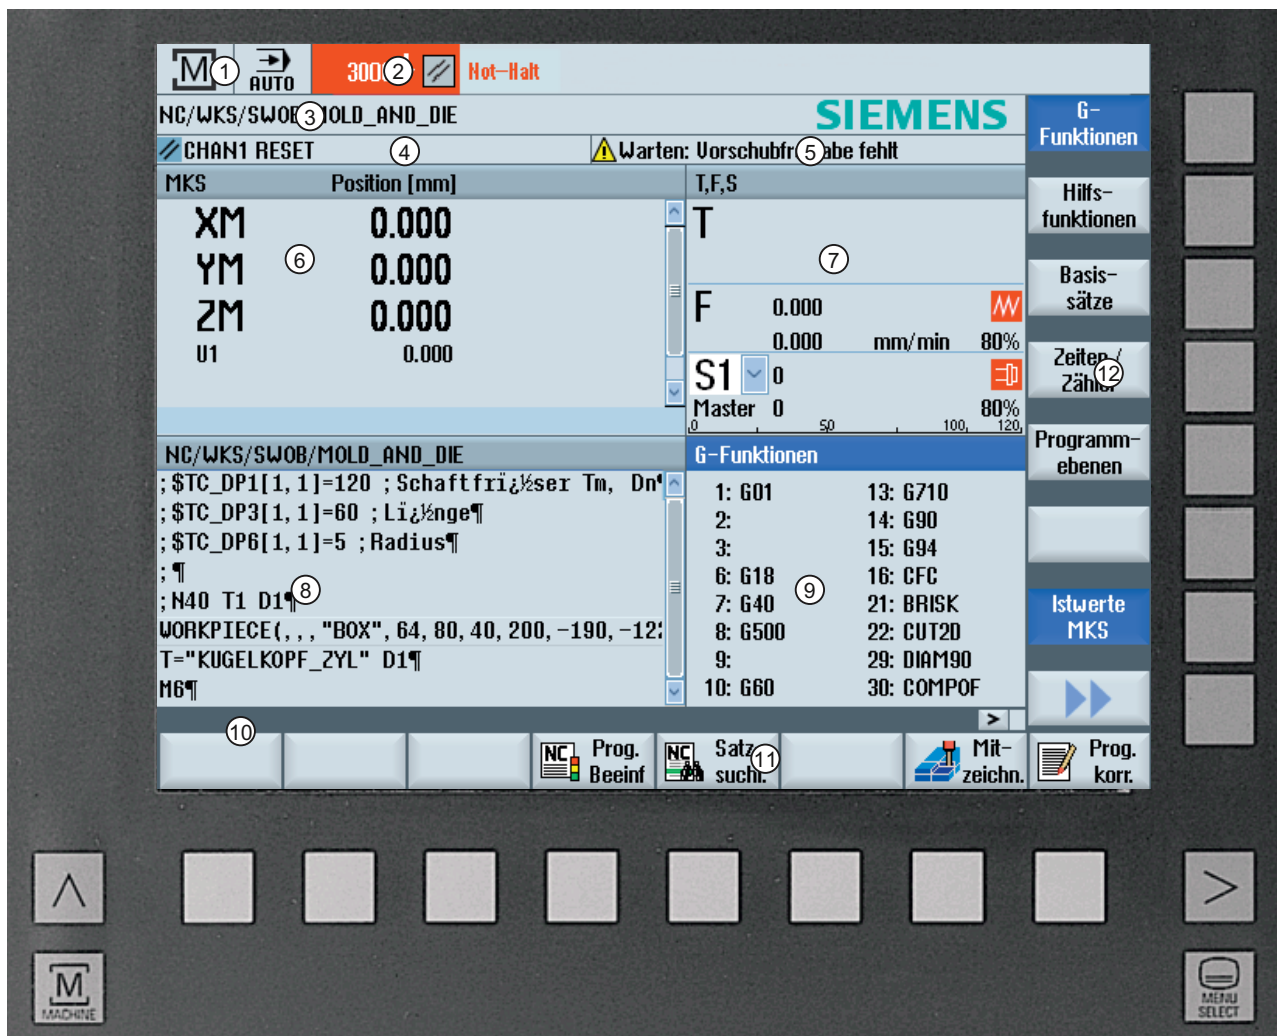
Vorderansicht Maschinensteuertafel (Ausführung Fräsen)
